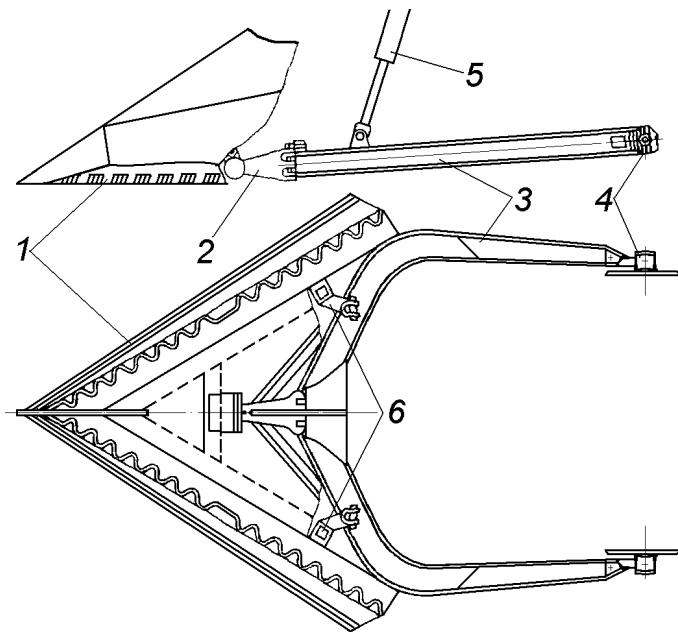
Рабочее оборудование кустореза: 1 – клиновидный кусторезный отвал; 2 – цапфа центрального сферического шарнира; 3 –
